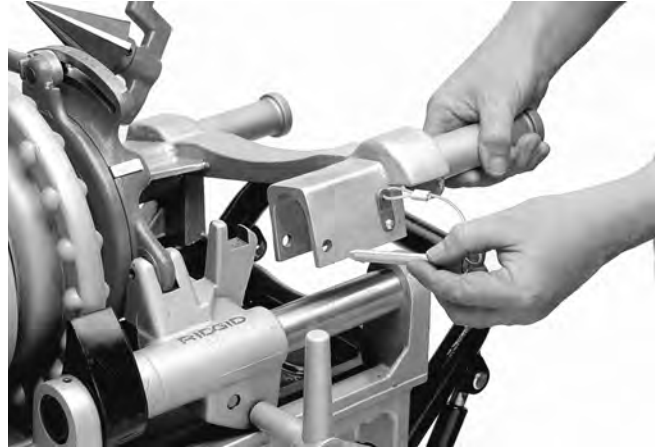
Montaje del Caballete Adaptador a la Máquina Roscadora No. 300 Compacta
